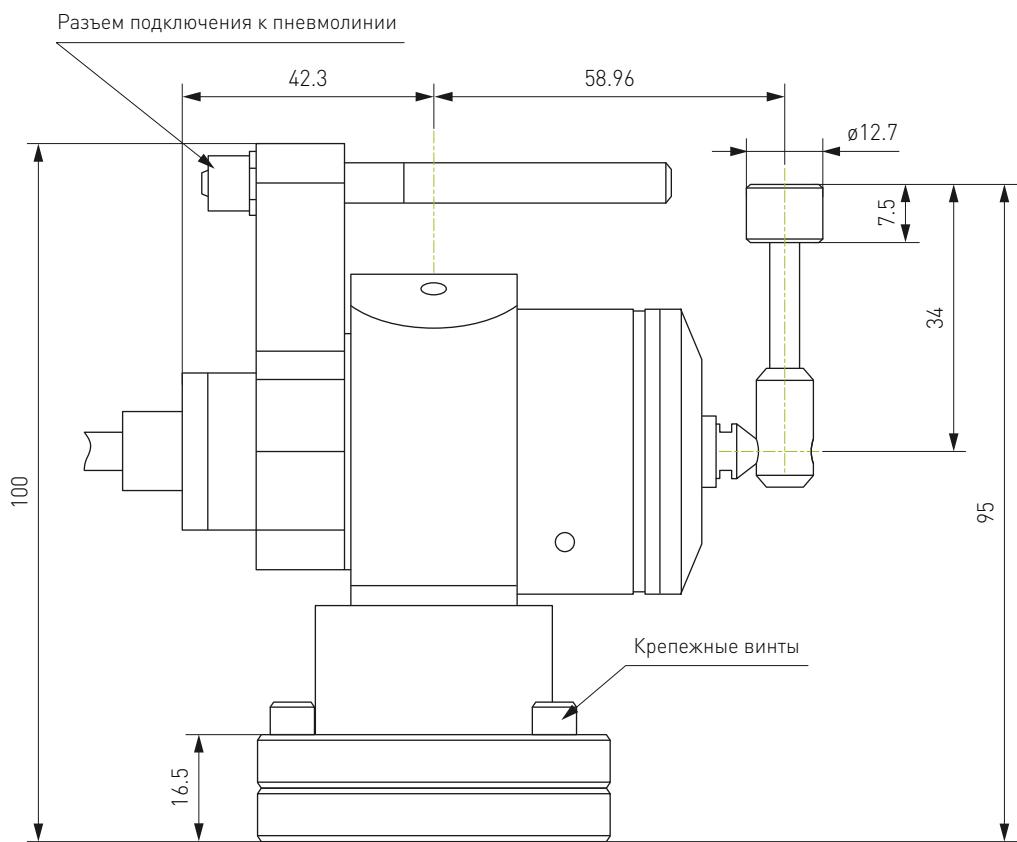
Габаритный чертеж датчика WT-12.7.
